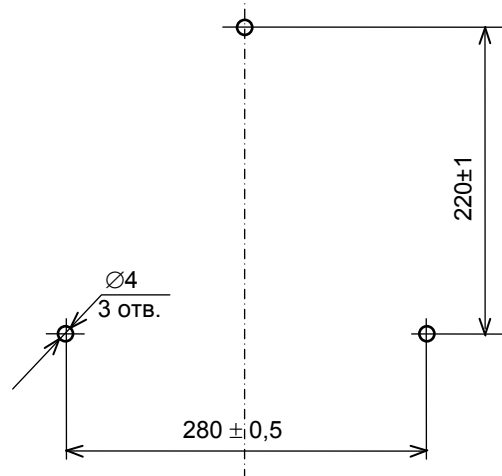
Разметка крепежных отверстий для установки прибора
